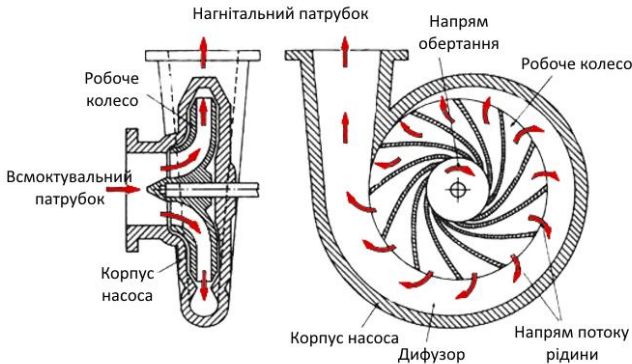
Схема робочого колеса відцентрового насоса
